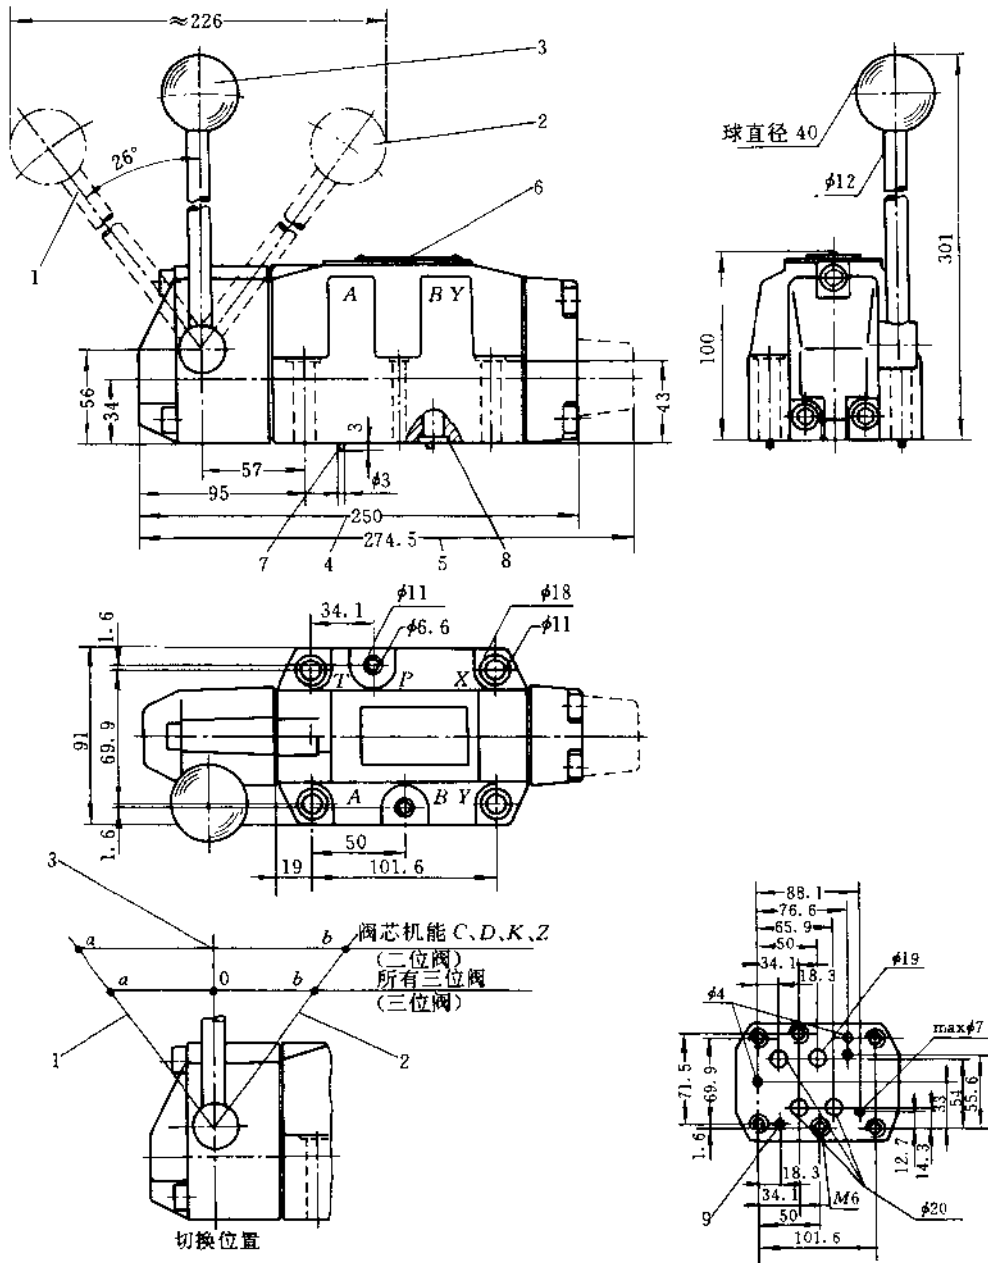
WMM16 手动换向阀外形及连接尺寸图
